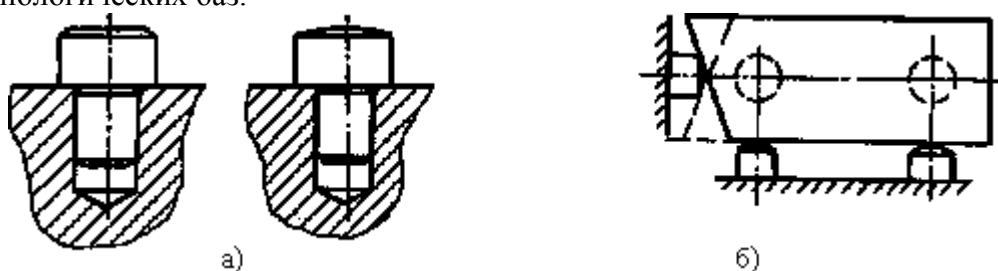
Опоры (а) и их установка (б) в приспособлении
